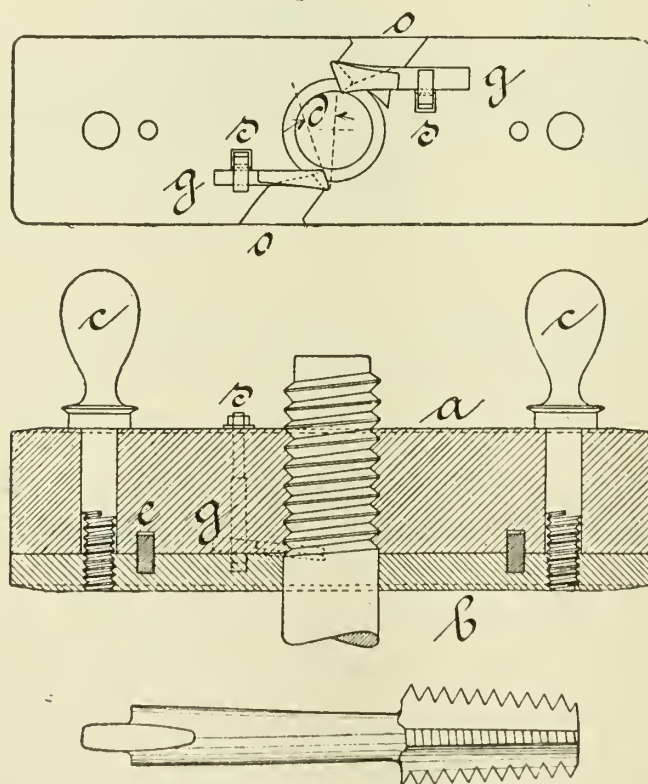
Holzschrauben-Schneidzeug samt Mutterbohrer.
